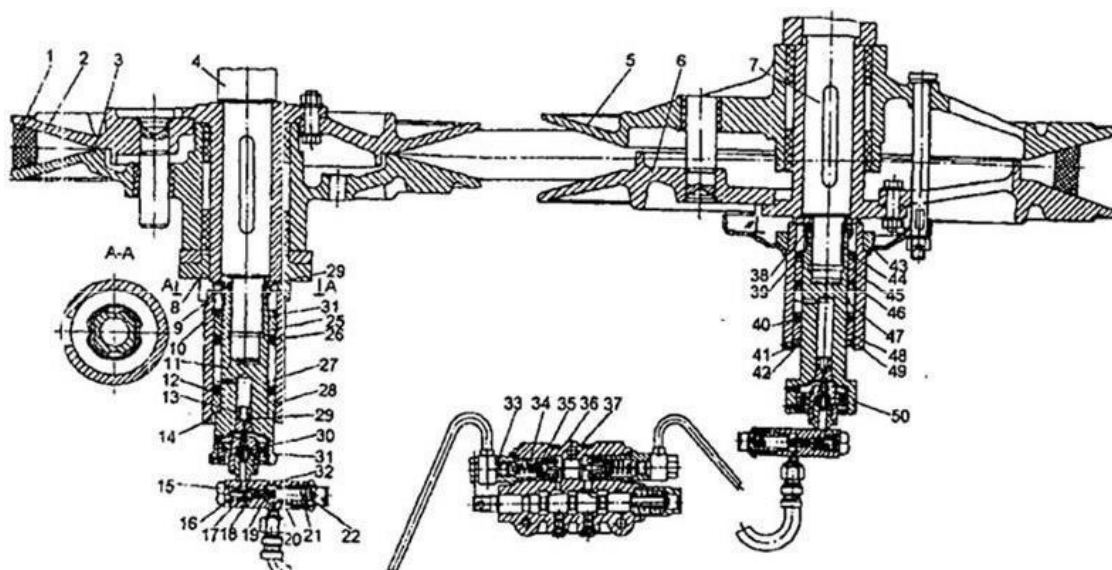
Гидрофицированный вариатор барабана:
